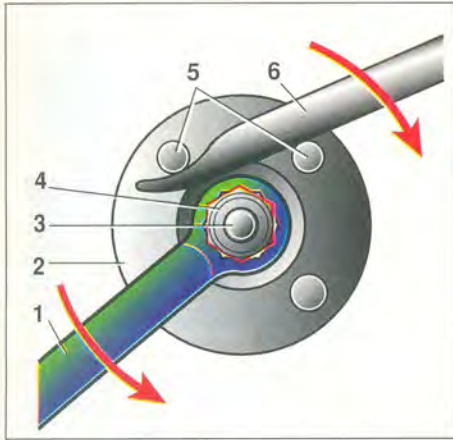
Способ отворачивания гайки ведущей шестерни: 1 – ключ; 2 – фланец; 3 – хвостовик; 4 – гайка М16х1,5; 5 – болты М8; 6 – монтажная лопатка.
